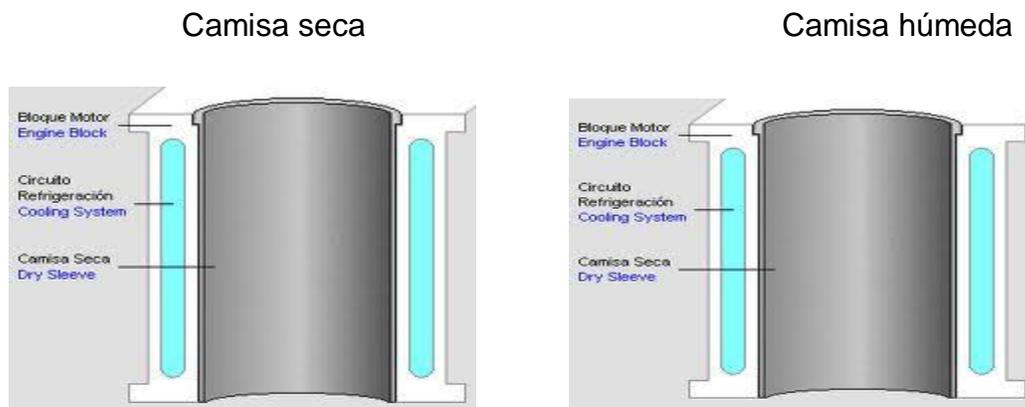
Normalmente está integrado directo con el Monoblock. Fig.3.34 Está en contacto Refrigerante del motor y es intercambiable.
